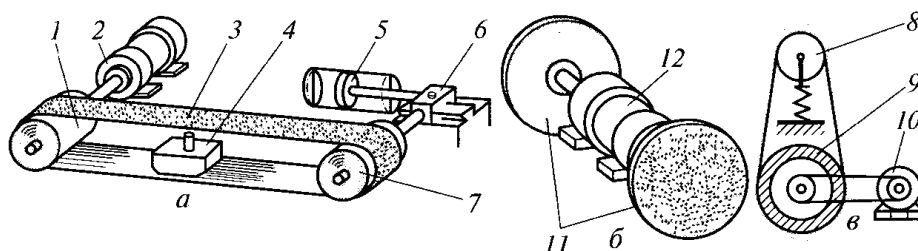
Робочі органи шліфувальних верстатів: а – вузькострічкових; б – дискових; в – широкострічкових; 1 – приводний шків; 2, 10, 12 – електродвигуни; 3 – шліфувальна стрічка; 4 – утюжок; 5 – пневмоциліндр; 6 – супорт; 7 – натяжний шків; 8 – натяжний ролик; 9 – контактний валець; 11 – диски
